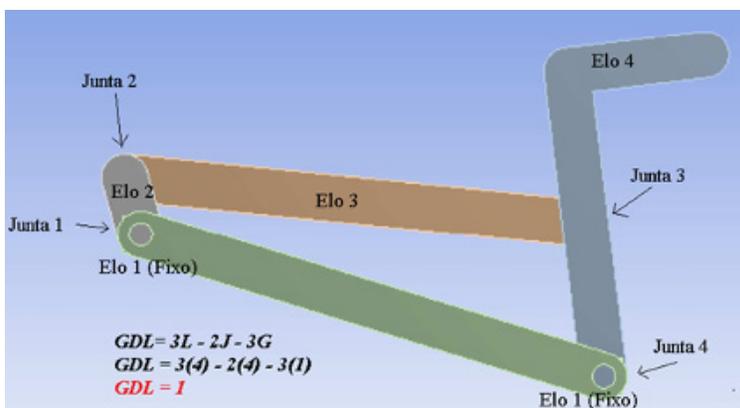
Mecanismo com saída do acoplador possuindo duas posições e movimento complexo.
